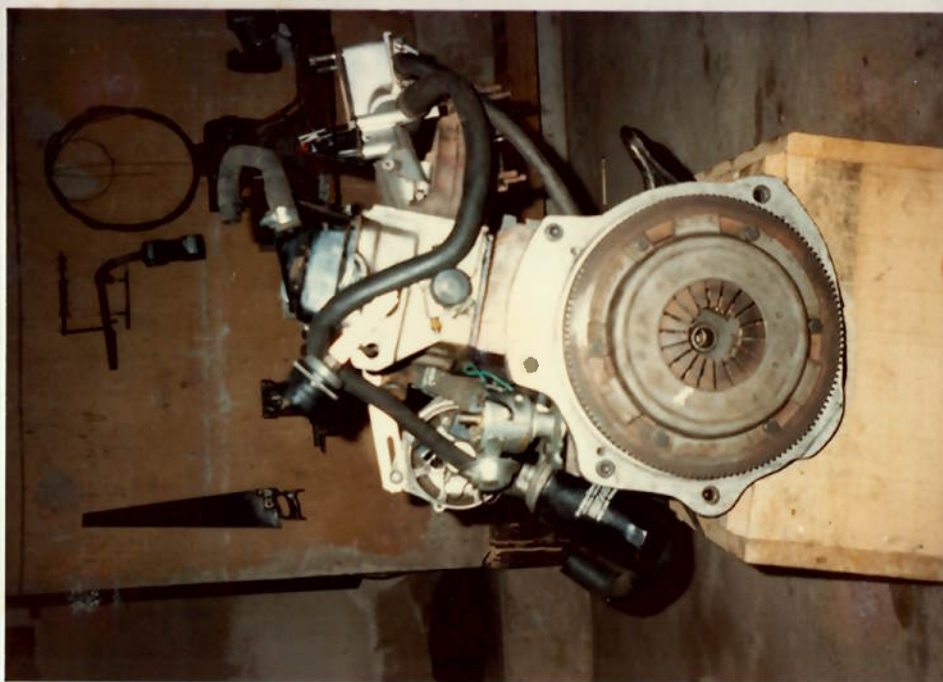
Vista frontal do motor mostrando o flange de adaptação à caixa de câmbio, o volante do motor e a embreagem.
